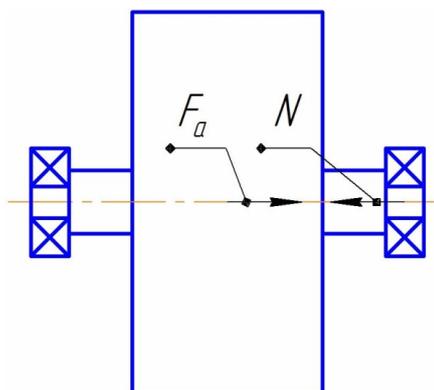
Схема нагружения подшипниковой опоры при установке подшипников с осевой игрой
